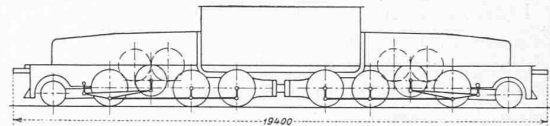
Güterzuglokomotive 1C+C1 der Maschinenfabrik Oerlikon für die Gotthardlinie der Schweizer. Bundesbahnen.
